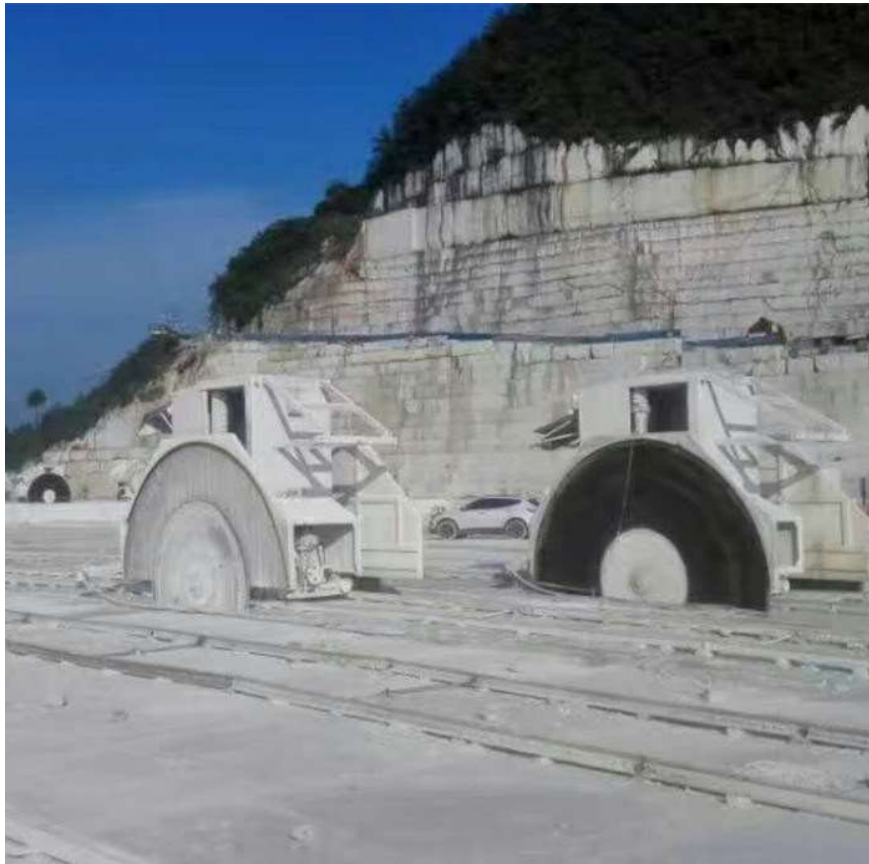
cortadora de disco. Fuente: es.made-in-china.com
